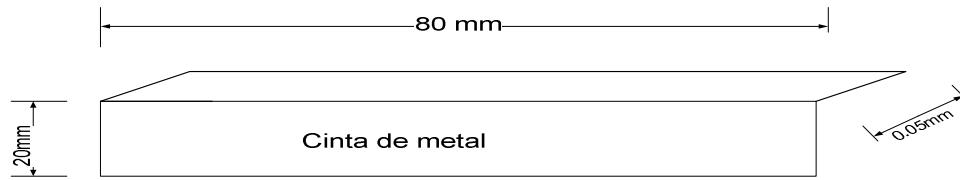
dimensiones de la Cinta de oro 12k , 18k , plata
